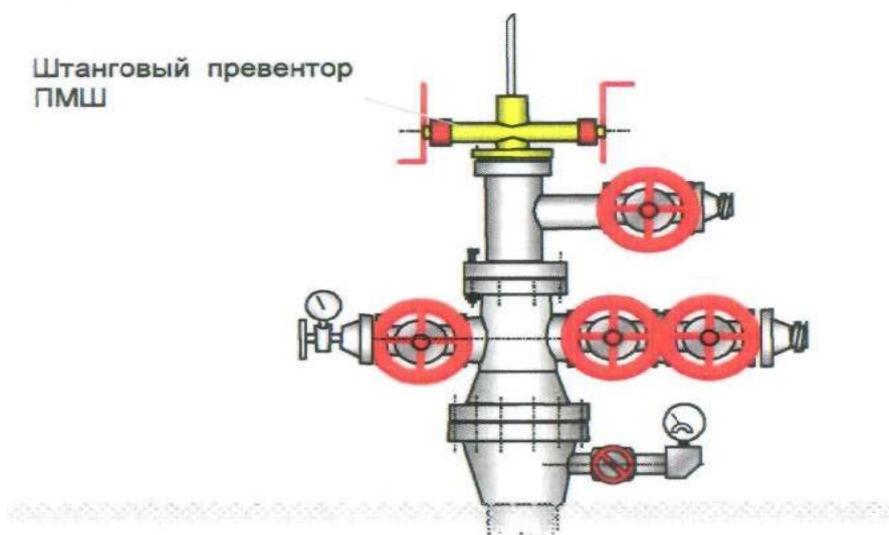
Схема монтажа ПВО №4 для скважин оборудованных штанговыми глубинными установками
